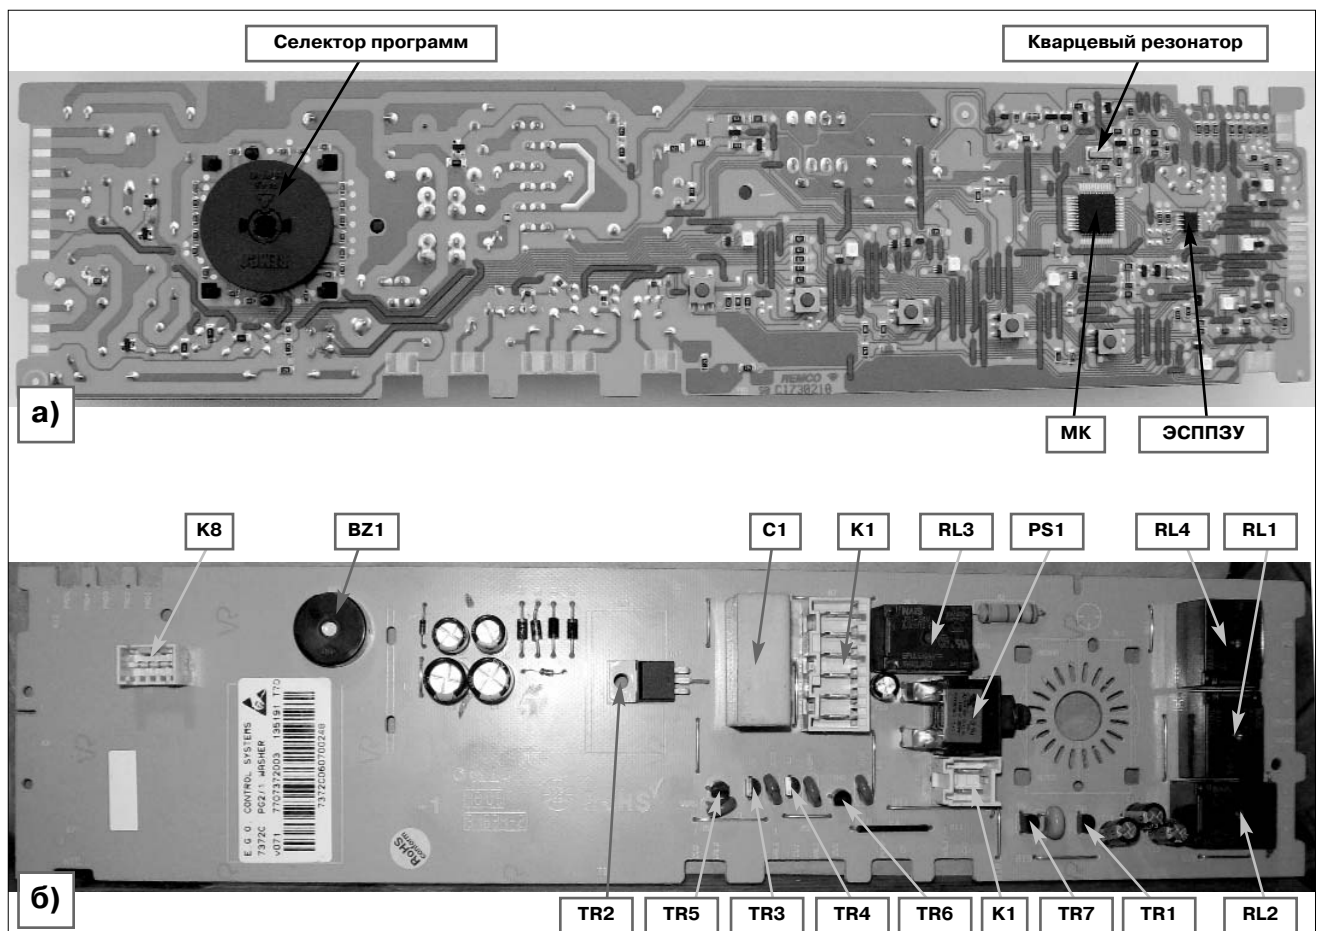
Внешний вид ЭМ PG-2: а — вид со стороны печатного монтажа; б — вид с лицевой стороны
